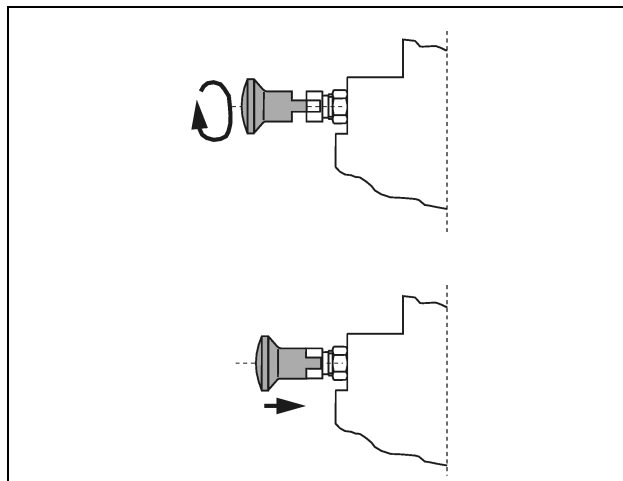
вверху: поверните фиксатор упорного болта на 90°, чтобы пазы располагались над выемками.
